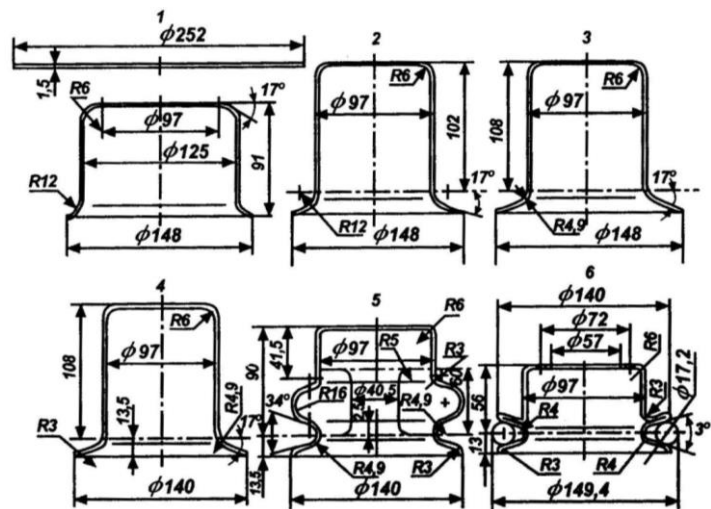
Технологічний процес штампування шківа: 1–3 – витягування; 4 – гнуття фланця; 5 – попереднє формування робочого струмка шківа; 6 – остаточне формування робочого струмка шківа
